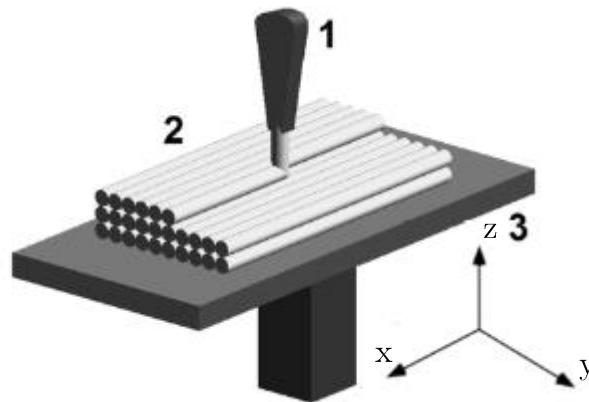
Esquema típico de la extrusión de materiales. 1) Boquilla u orificio de extrusión. 2) Material depositado. 3) Plataforma de construcción [39].
